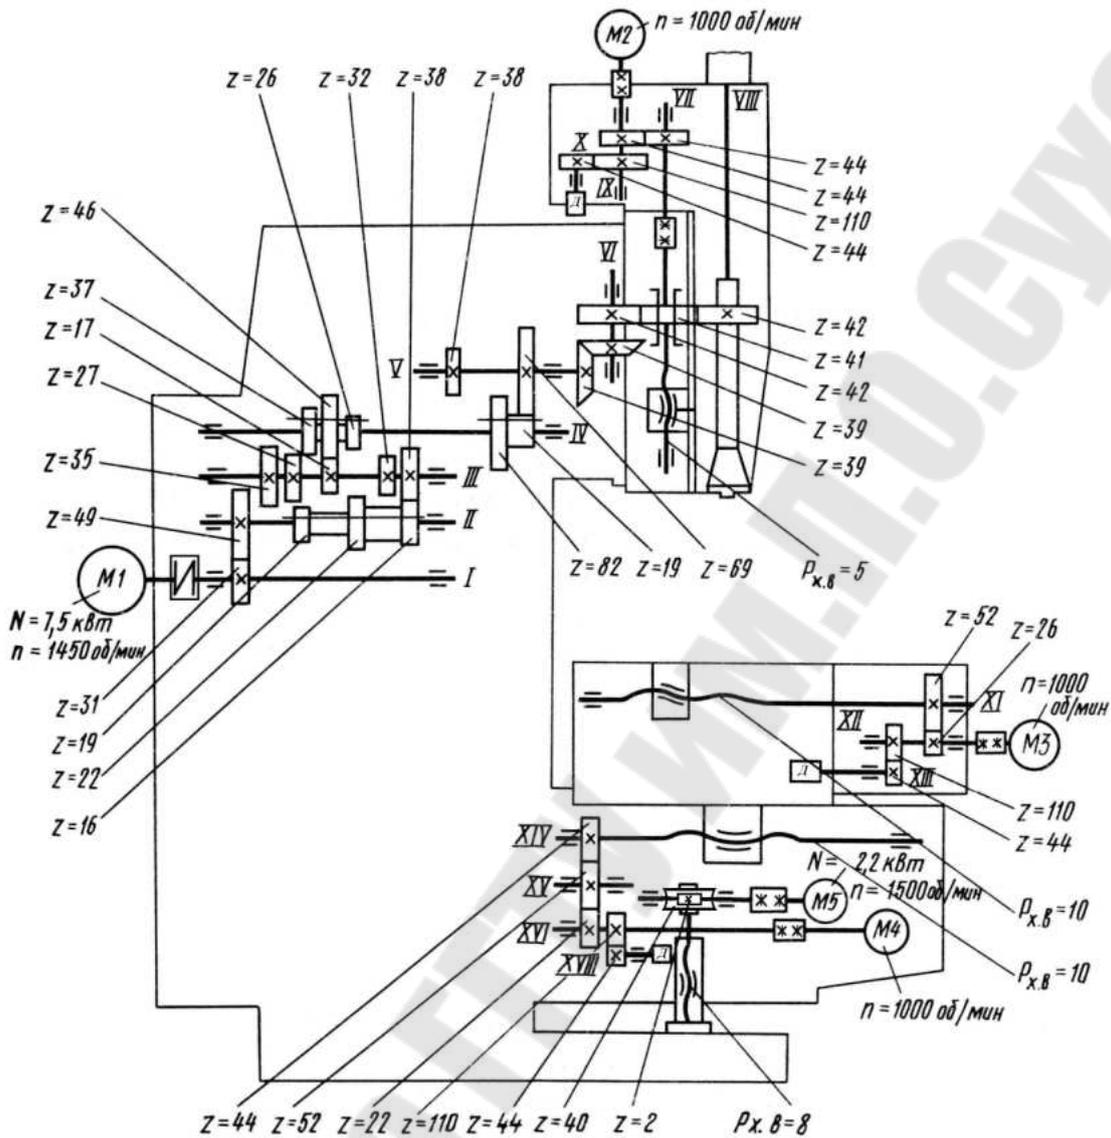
Кинематическая схема вертикально-фрезерного станка с ЧПУ 6Р13Ф3-37
